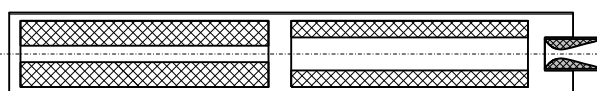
Пороховой заряд с двумя различными цилиндрами
